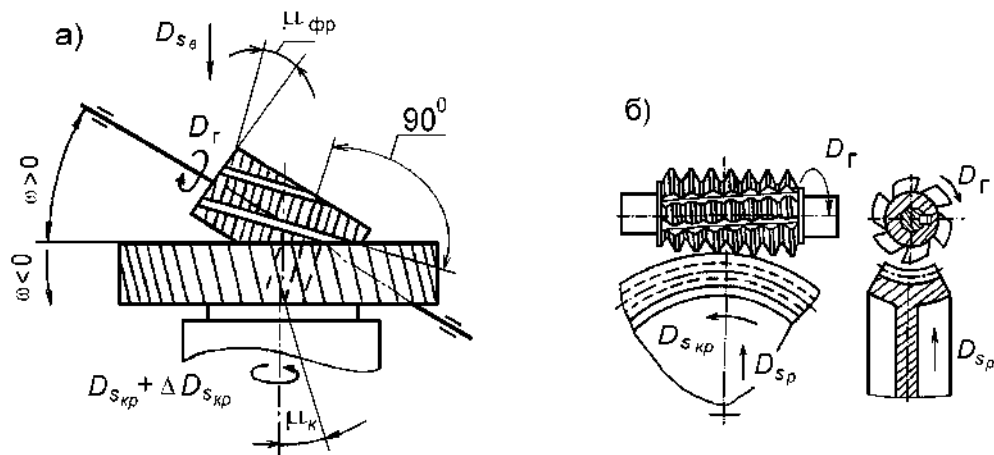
Схема нарізування зубчастого колеса черв'ячною фрезою
